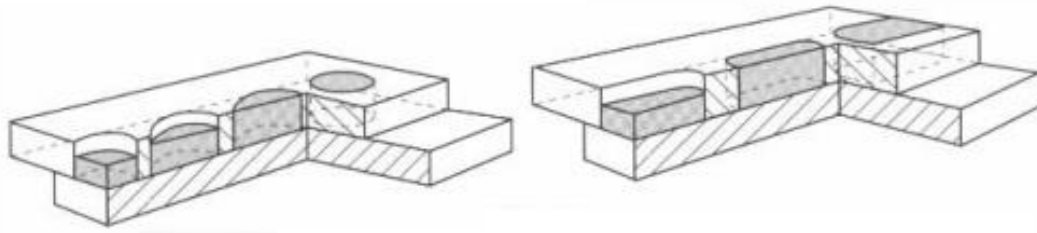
Tipo de Soldadura en botón y en ranura; izquierda: soldadura en botón, derecha: soldadura en ranura.
